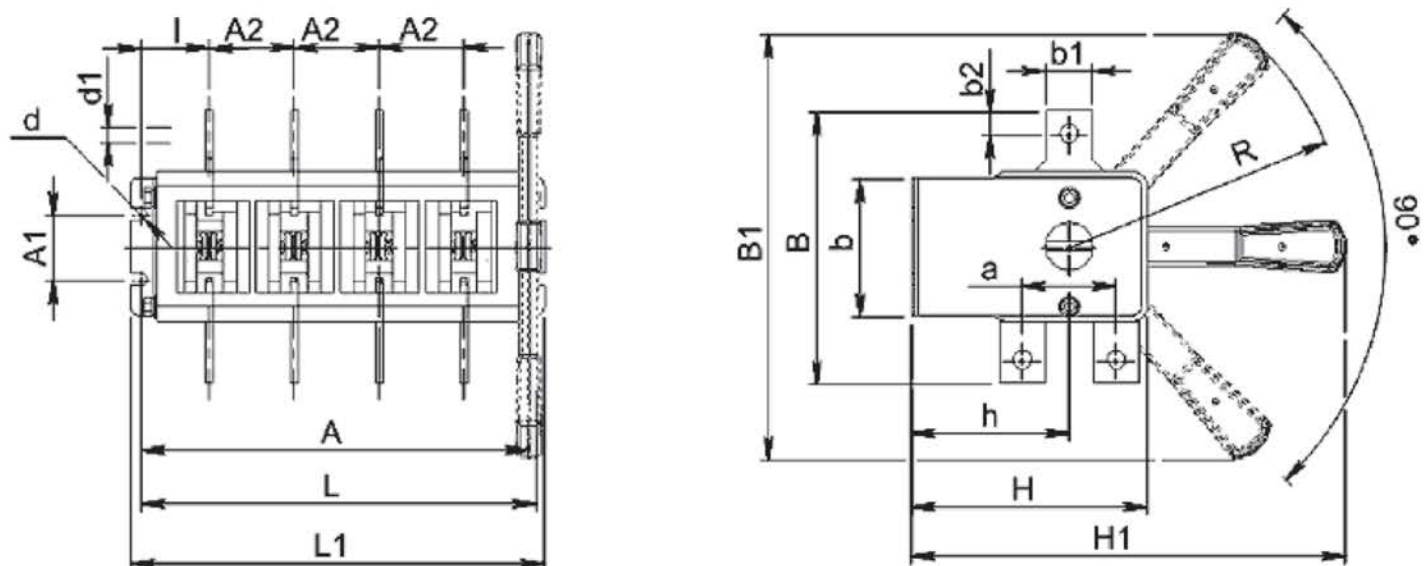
Выключатель-разъединитель четырехполюсный на два направление с боковой смещенной рукояткой.
